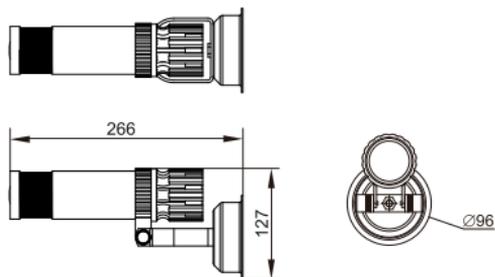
Габаритные размеры LPRO002-01-10-035-20-K03
